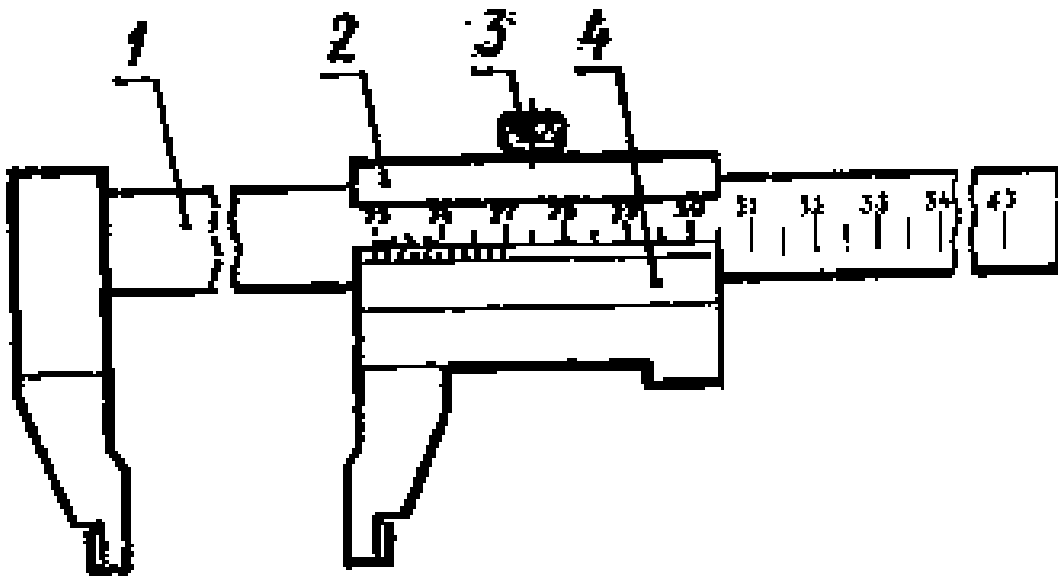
Штангенциркуль ШЦ-III: 1 – штанга; 2 – рамка; 3 – затискувач рамки; 4 – ноніус
